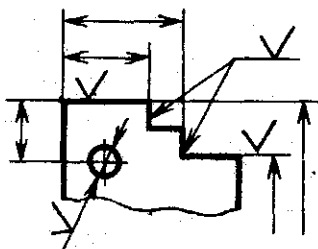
Методы расположения обозначения шероховатости поверхности детали при недостатке места на изображении чертежа
